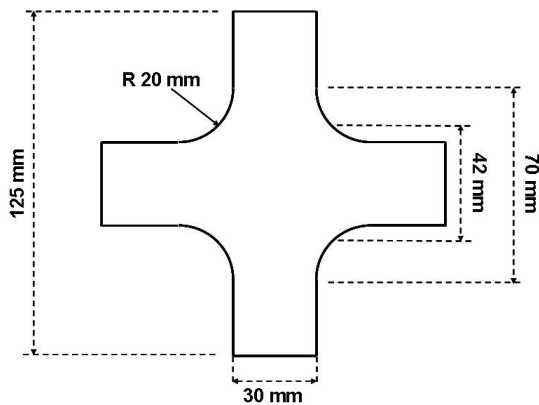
Géométrie : éprouvette en forme de croix.
